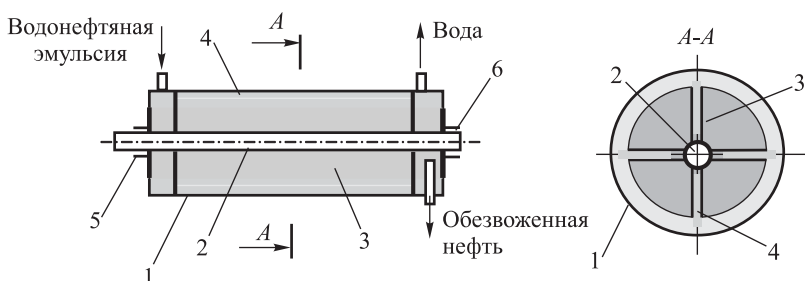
Центробежный делитель фаз: 1 — корпус; 2 — вал; 3 — неподвижные лопасти; 4 — подвижные лопасти; 5, 6 — сальниково-подшипниковые узлы
